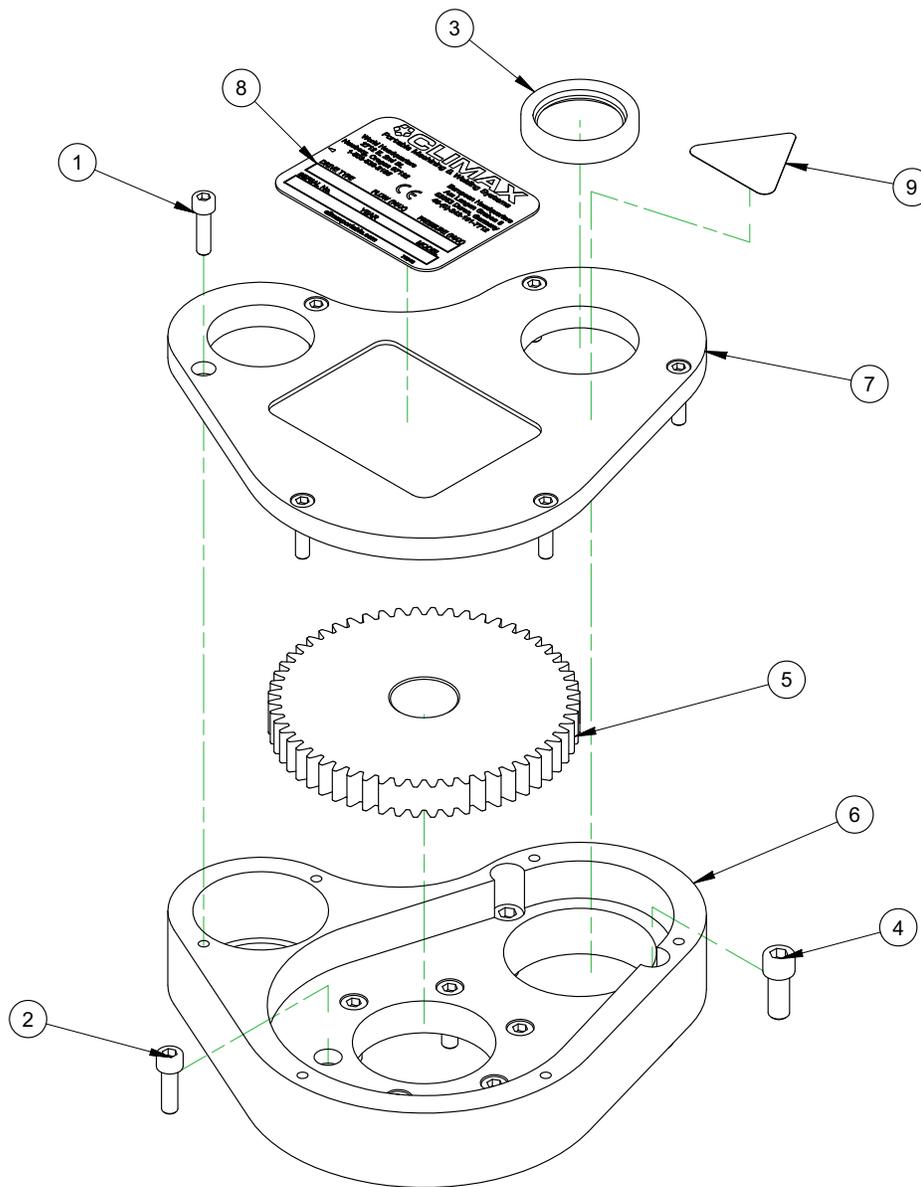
ENSEMBLE DE MOTEUR PNEUMATIQUE (RÉF. 38708)
